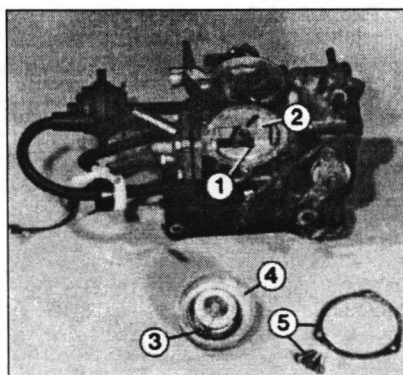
А.8 Крышка стартера (4) в карбюраторе двигателя мощностью 44 кВт крепится к корпусу карбюратора с помощью удерживающего кольца и винтов со шлицевой головкой (5). При установке, нельзя забывать о том, что поводок (2) карбюратора входит в зацепление, в проушину (3) биметаллической пружины. В позиции 1, показана переключающая штанга мембраны Pyldown, которая слегка приоткрывает закрытую воздушную заслонку после запуска двигателя.
